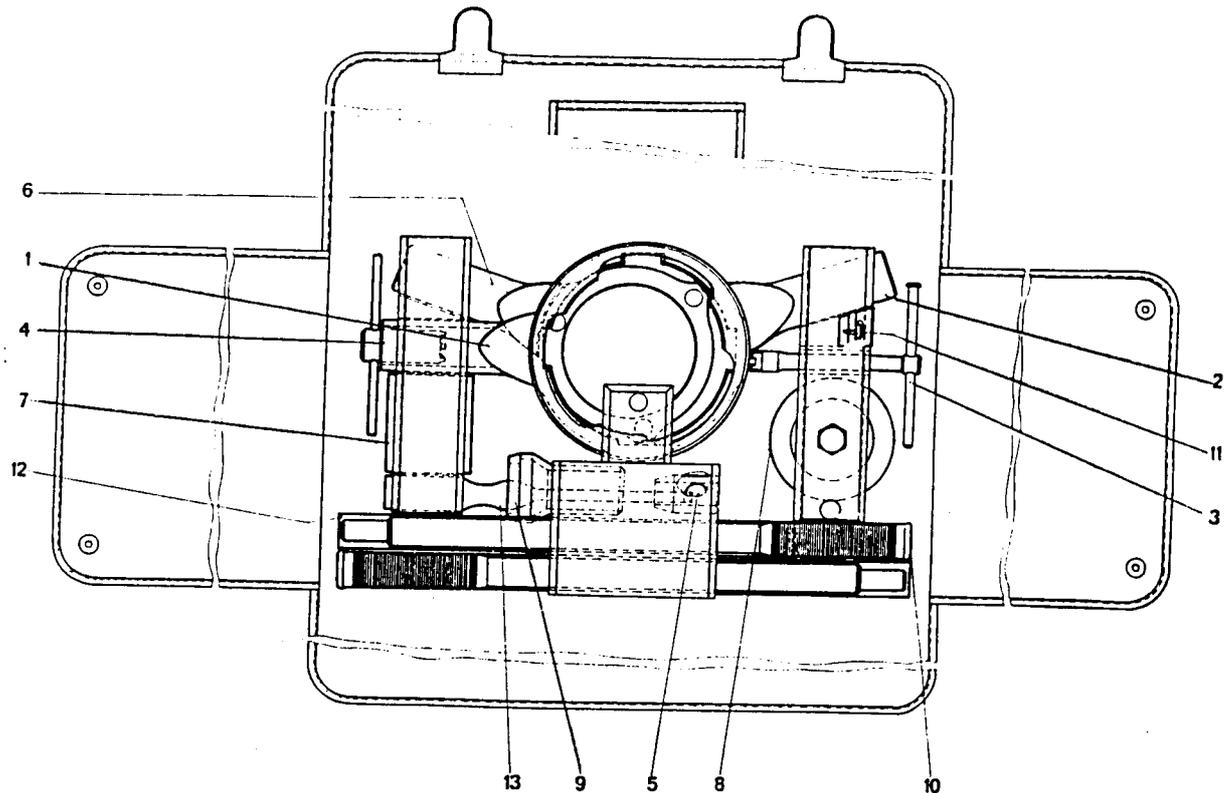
Montagewerkzeug für Luftschraube V 503 A in der Werkzeugtasche Satz „A“
